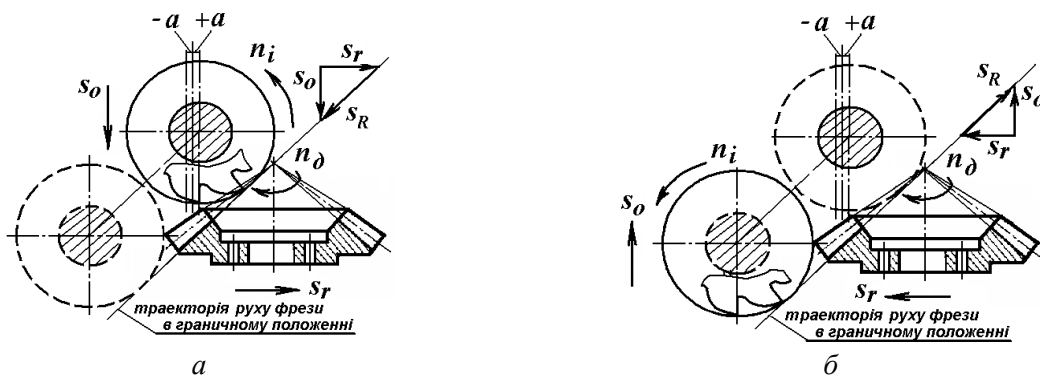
Кінематичні схеми нарізання конічних коліс на зубофрезерному верстаті дисковою фрезою за неперервного обкочування на основі радіально-колового способу
